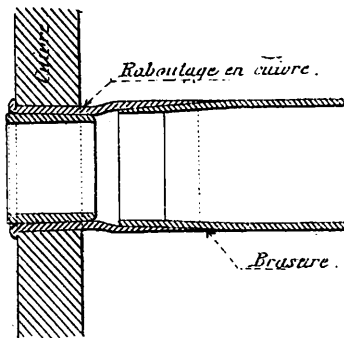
bis*. — Tube à air chaud de la compagnie de Lyon (côté du foyer).
